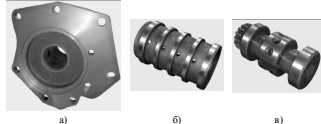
Детали топливной аппаратуры: корпус а), втулка б), золотник в)
